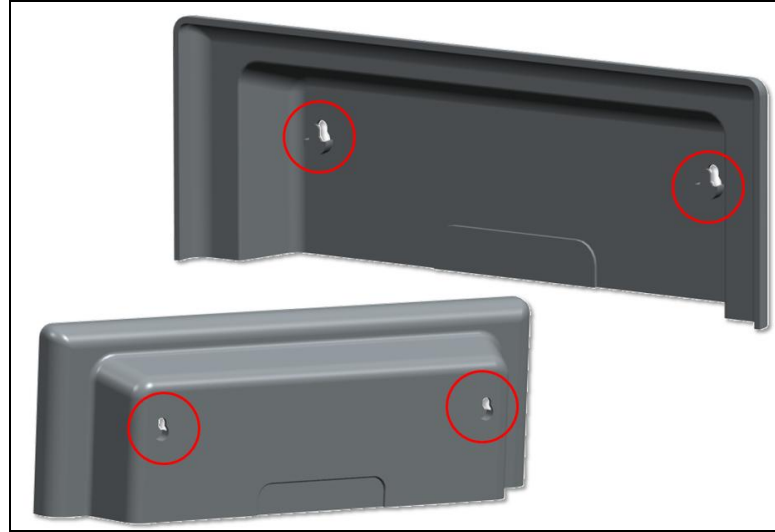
59 Arka kapak dış yüzeyinde Side AV PCB için yapılan boşaltmalar
